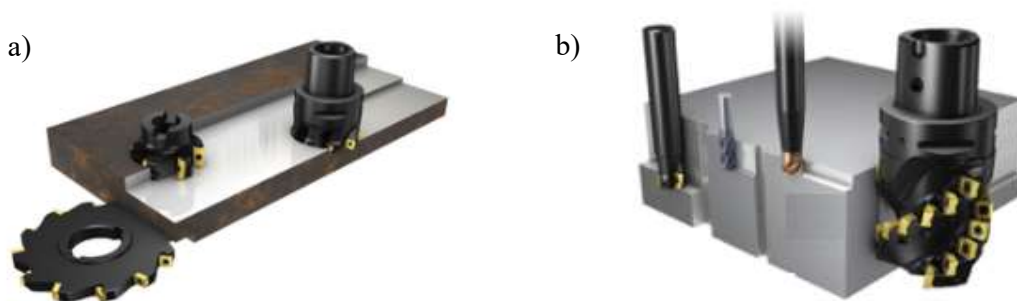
a) frézování drážky b) frézování tvaru [18]
